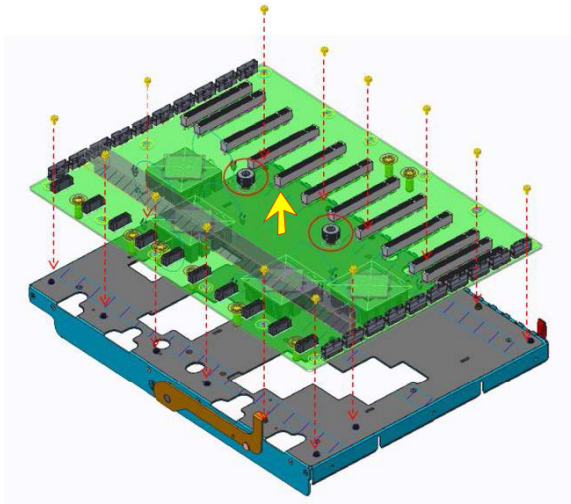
Befestigungsschrauben der PCIe-Schaltplatine entfernen
